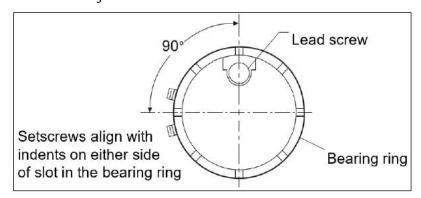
TORNILLO GUÍA (ARRIBA) Y ANILLO DE RODAMIENTO (DERECHA)
